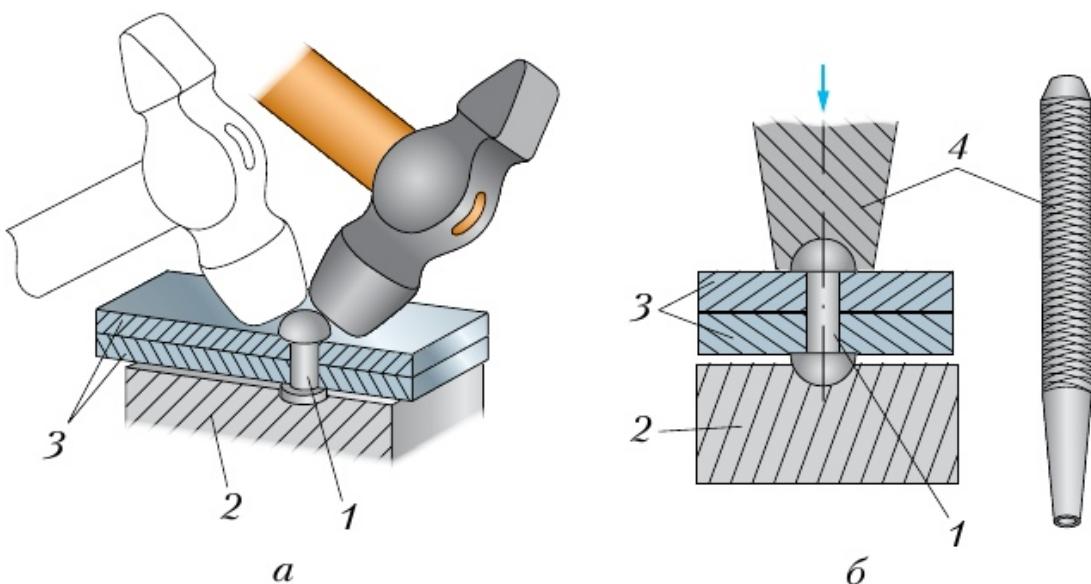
Примеры соединения деталей из тонколистового металла:
